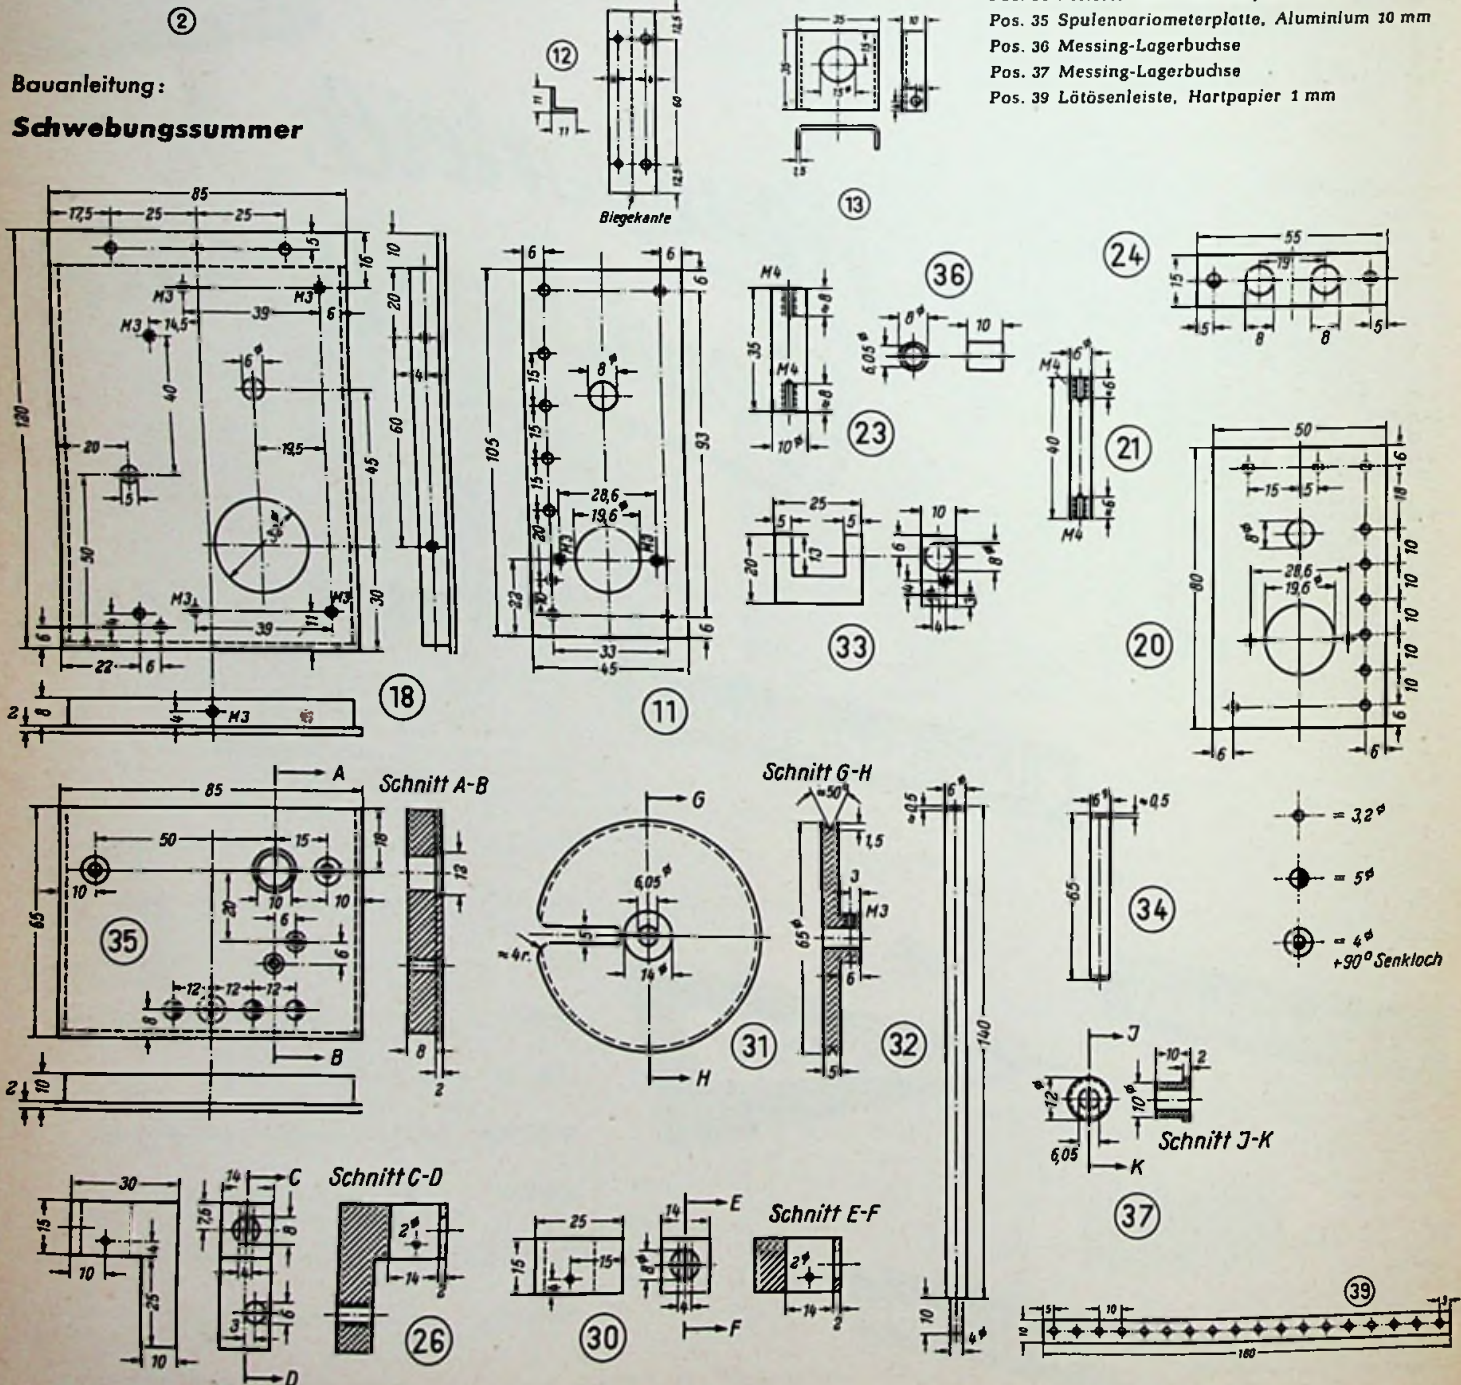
Maßzeichnungen für die wichtigsten Bauteile
